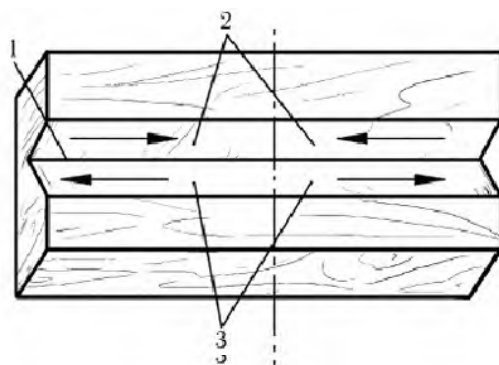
Выполнение прямой двусторонней выемки, направленной вдоль волокон заготовки из свилеватой древесины (стрелками показано направление движения инструмента)
